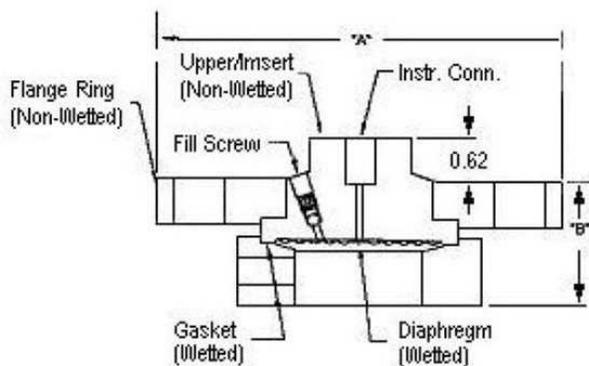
Dimensiunile Flanselor cu Diafragme Incapsulate(Flush Flanged)
